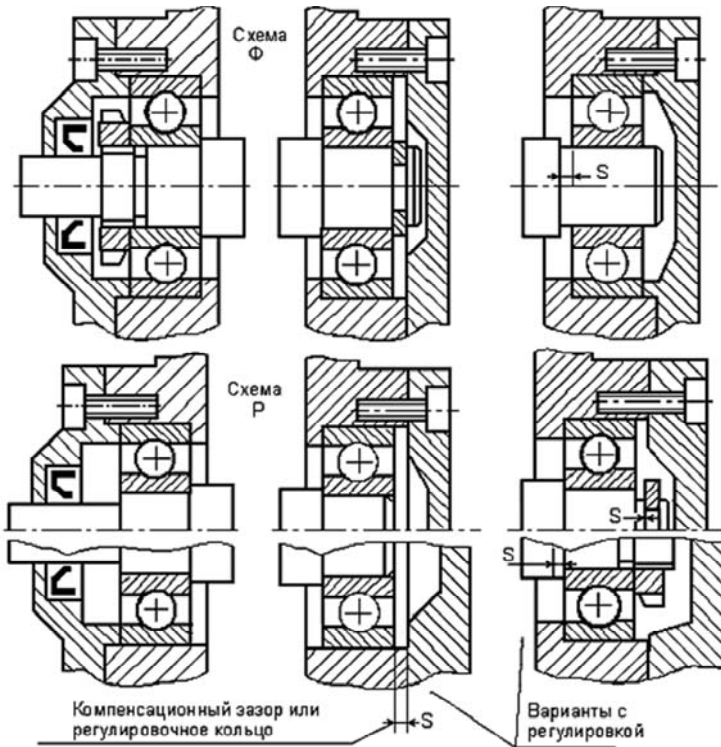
Примеры конструкции опор с различными схемами установки
